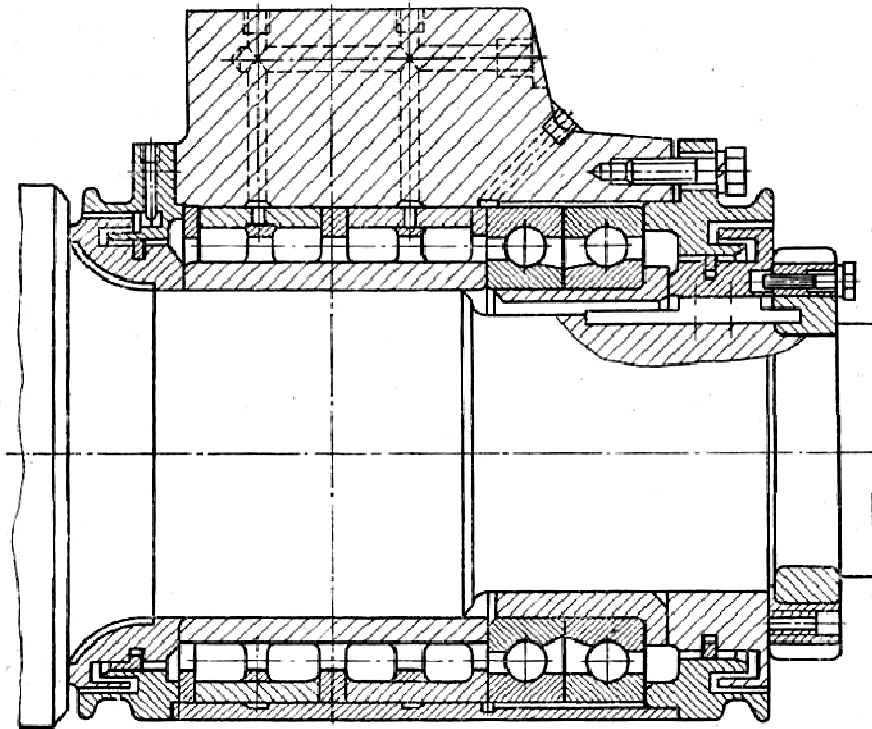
Фіксуєча опора валка на чотирирядному підшипнику із циліндричними роликами
